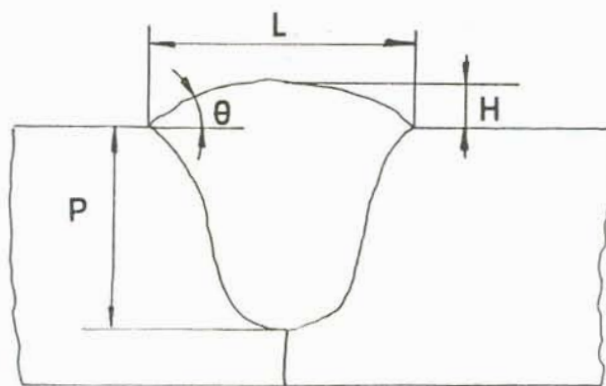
Definição de algumas características geométricas do cordão soldado: L-largura do cordão; θ -ângulo de molhamento ou contato do cordão; H-altura do reforço do cordão; P-penetração.
